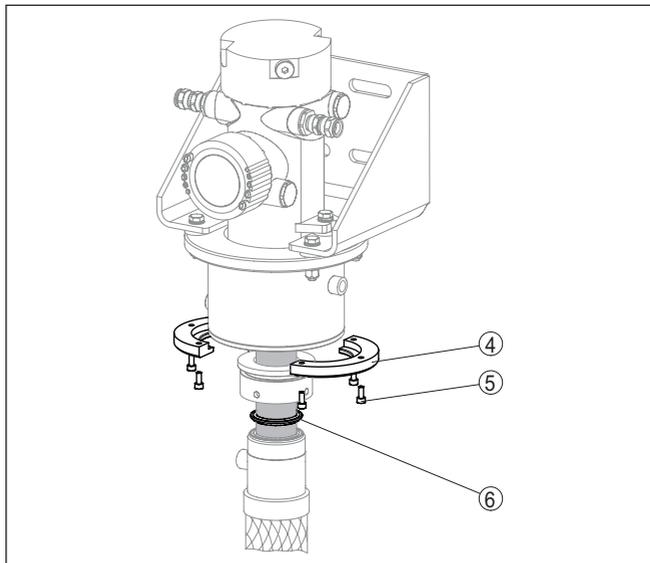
Kit de montage - flexible réfrigérant du scintillateur - haut
